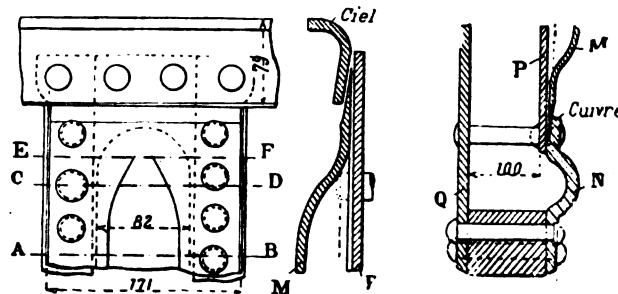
, 37 e 38. — Particolari del focolaio Laughridge.
